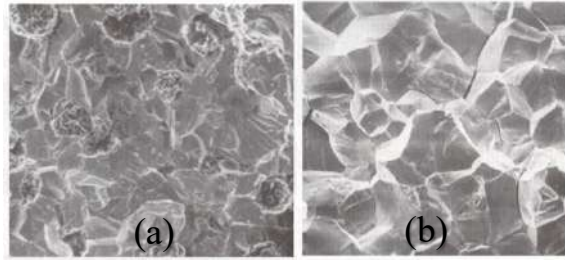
(a) fractura intergranular, (b) fractura transgranular [8]
